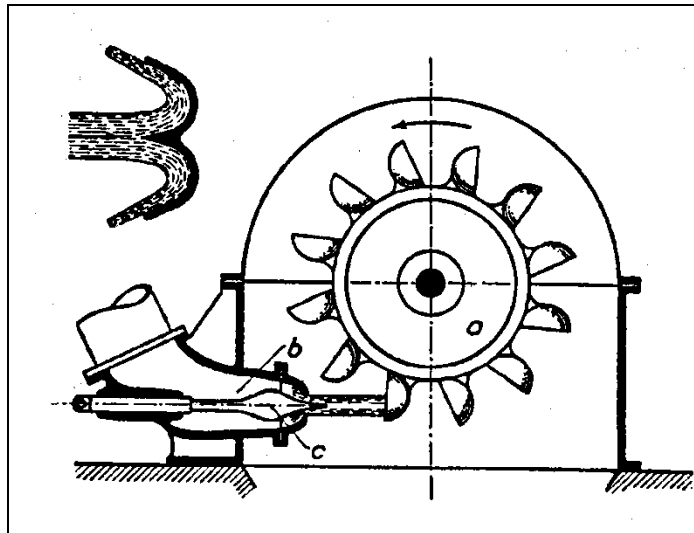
Prinzipskizze einer Pelton-Turbine: Das Wasser strömt aus der Düse (b), der Menge nach geregelt durch die Nadel (c), etwa tangential gegen die Schaufeln des Rades (a). Der Stahl wird auf die Schneide der Schaufeln gerichtet und durchströmt, sich teilend, die beiden Schaufelmulden, wobei die Strahlhälften um fast 90 Grad aus ihrer absoluten Bahn seitlich abgelenkt werden. (aus: HOFFMANN 1962)
